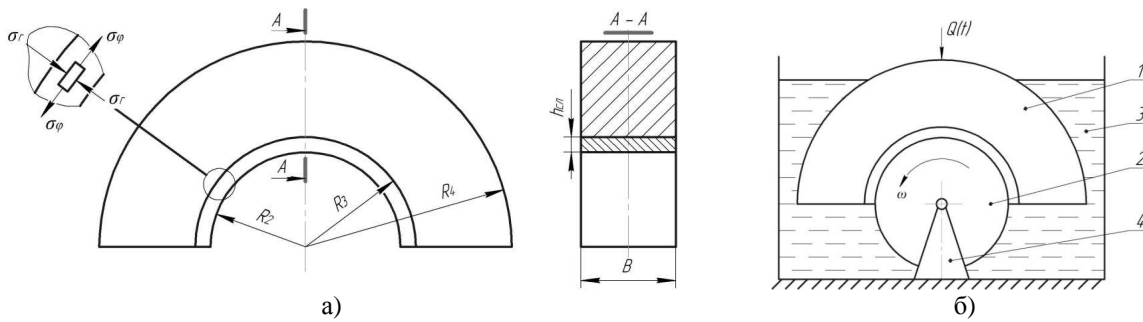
Полукольцевой подшипник-образец (а) и схема его нагружения (б)
